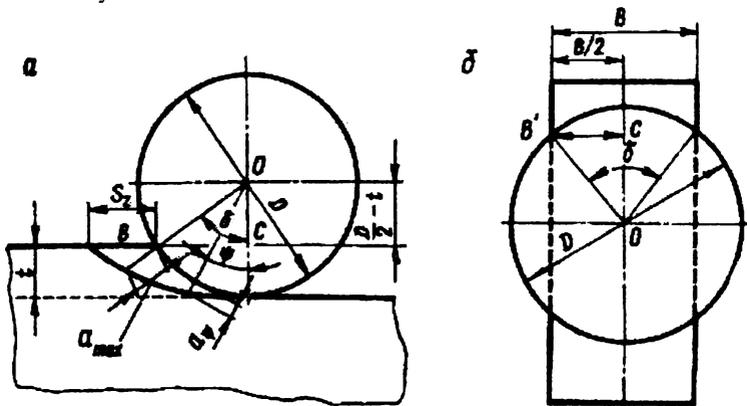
Схема резания при цилиндрическом (а) и торцевом (б) фрезеровании
